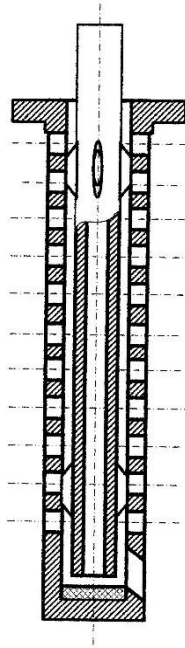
Схема устройства для отбора пробы молока из емкости
